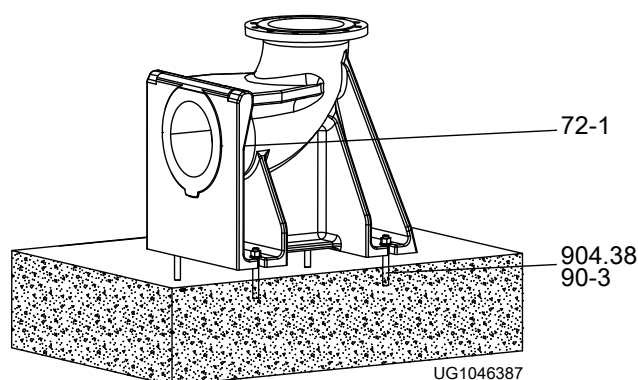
Крепление опорного фланцевого колена соединительными анкерами
